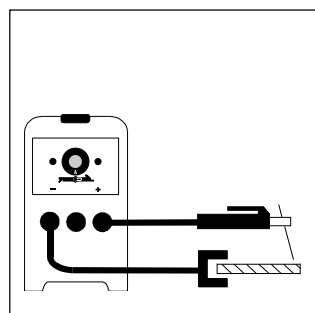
TP 1400 MV ausgerüstet zum E-Handschweißen
